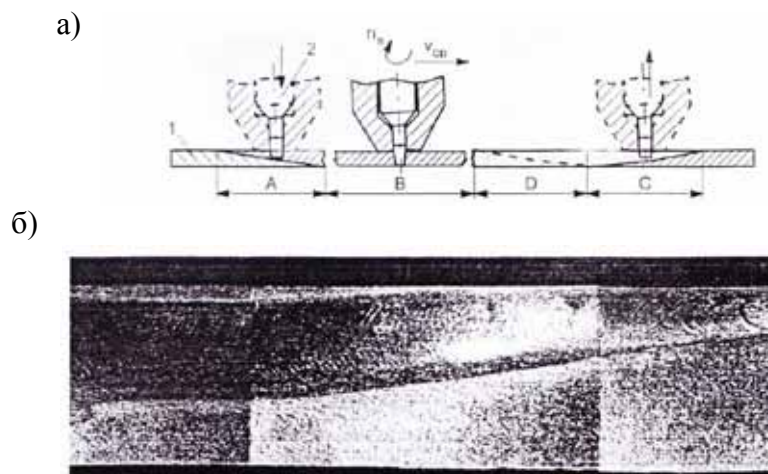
Схема введения в стык и выведения из него рабочего стержня сварочного инструмента (а) (А, С – зоны ввода и вывода инструмента, В – зона шва без перекрытия, D – зона перекрытия начала шва): 1 – листовая заготовка ( $\delta = 4$  мм); 2 – инструмент, продольный макрошлиф конечного
